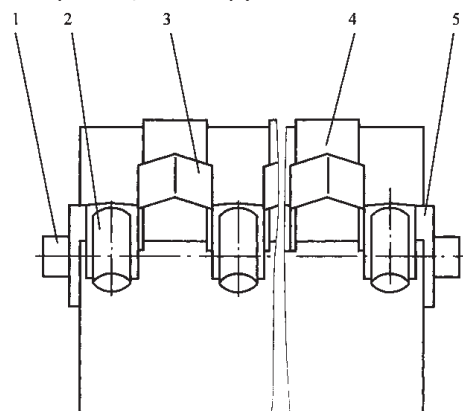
Схема размещения приспособления для очистки шламособорных цилиндрических магнитных дисков и шнеков (вид сбоку)
